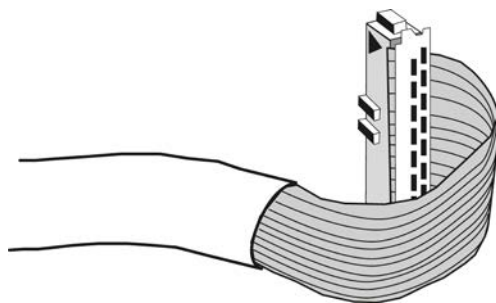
Flachrundleitung über Steckerobenseite zurückführen
